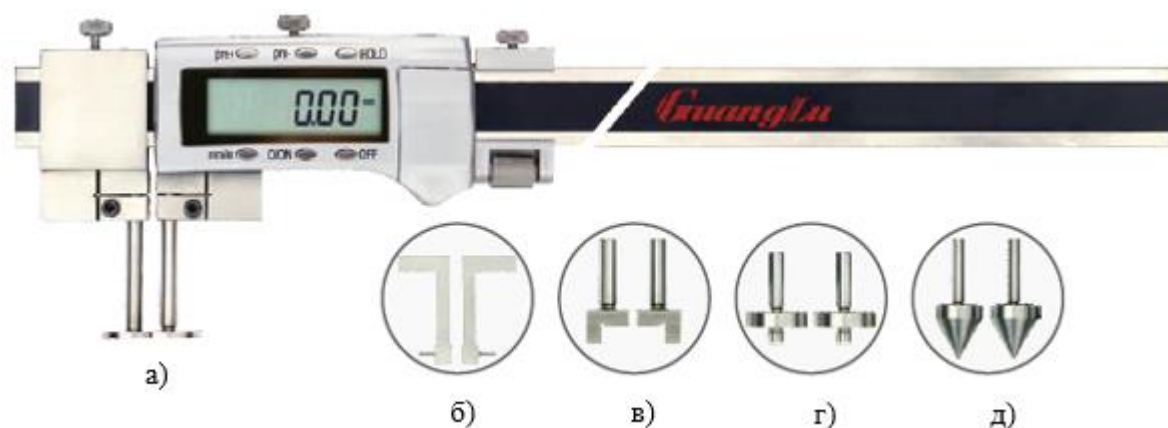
Общий вид штангенциркулей модификации 118, исполнения 455 и комплекты сменных измерительных губок; а) – тарельчатые с плоскими измерительными поверхностями; б) – цилиндрические с точечными измерительными поверхностями; в) – г-образные с плоскими измерительными поверхностями; г) – тарельчатые с точечными измерительными поверхностями; д) – цилиндрические с коническими измерительными поверхностями для определения расстояния между центрами отверстий
